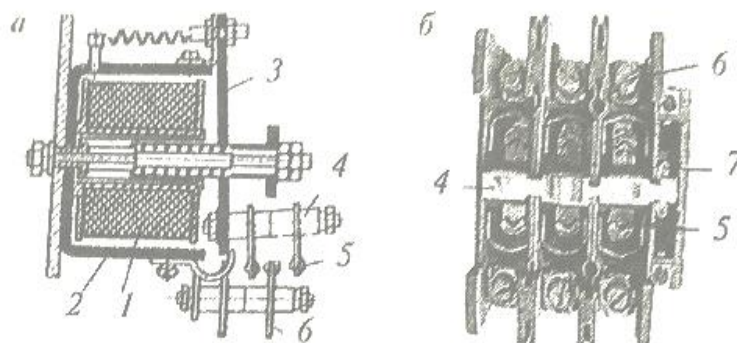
Принцип работы контактора (а) магнитного пускателя и внешний вид траверсов (б)
